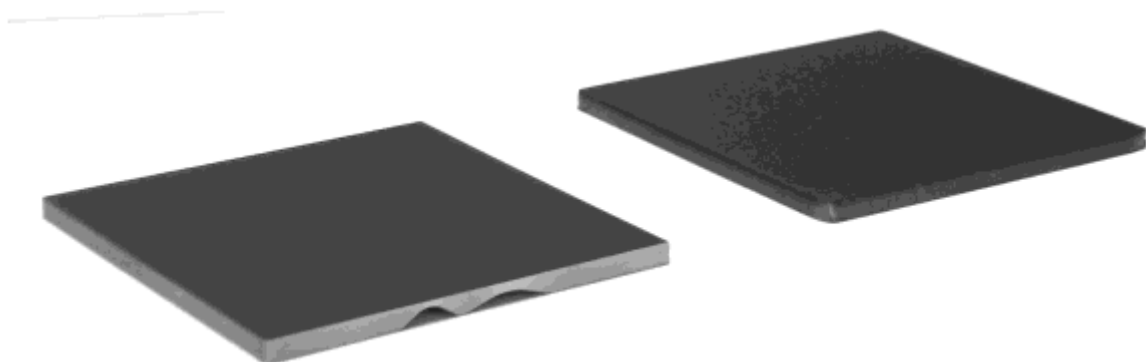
Fotos der Stahlprobe mit einer künstlich erzeugten Korrosionskontur (links) und der Referenzprobe (rechts)
